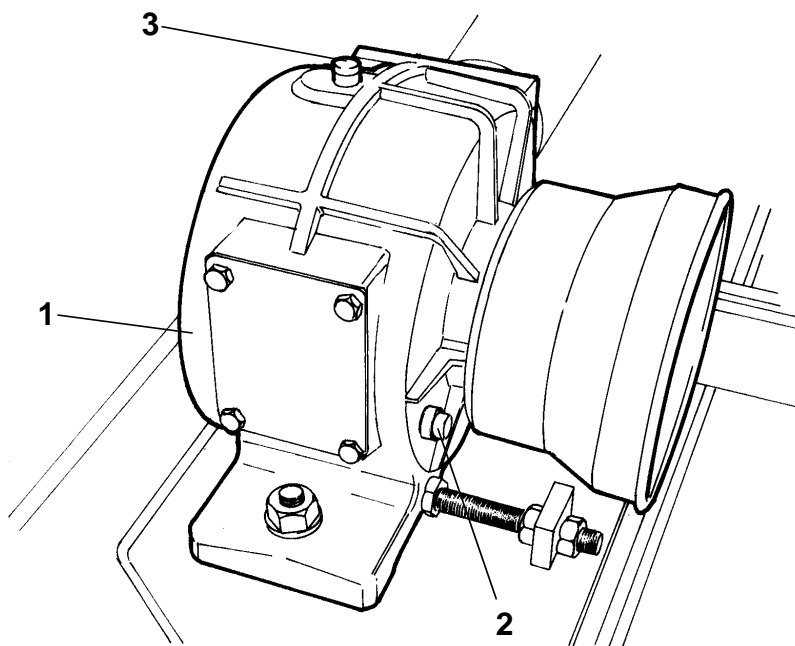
Controllo livello olio scatola ingranaggi - Inspection of oil level in gearbox
